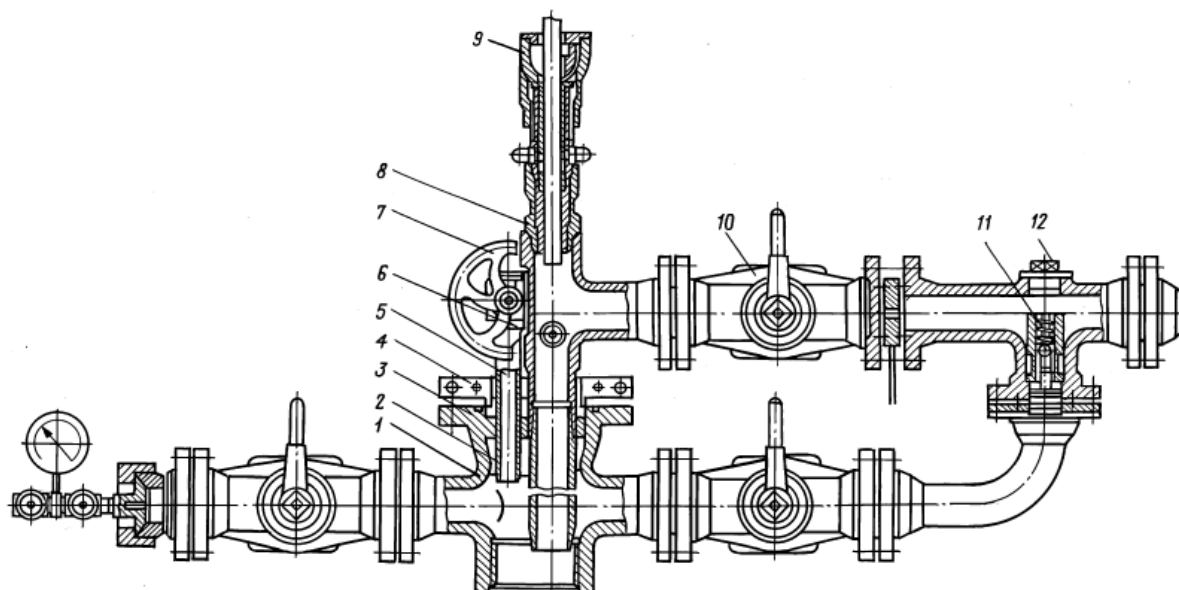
Оборудование устья ОУ140-146/168-65Б: 1 - крестовик; 2 - конусная подвеска; 3 - резиновые уплотнения; 4 - разъемный фланец; 5 - патрубок; 6 - тройник; 7 - задвижка; 8 - сальник устьевого СУС2; 9, 11 - обратный клапан; 10 - кран; 12 – пробка
